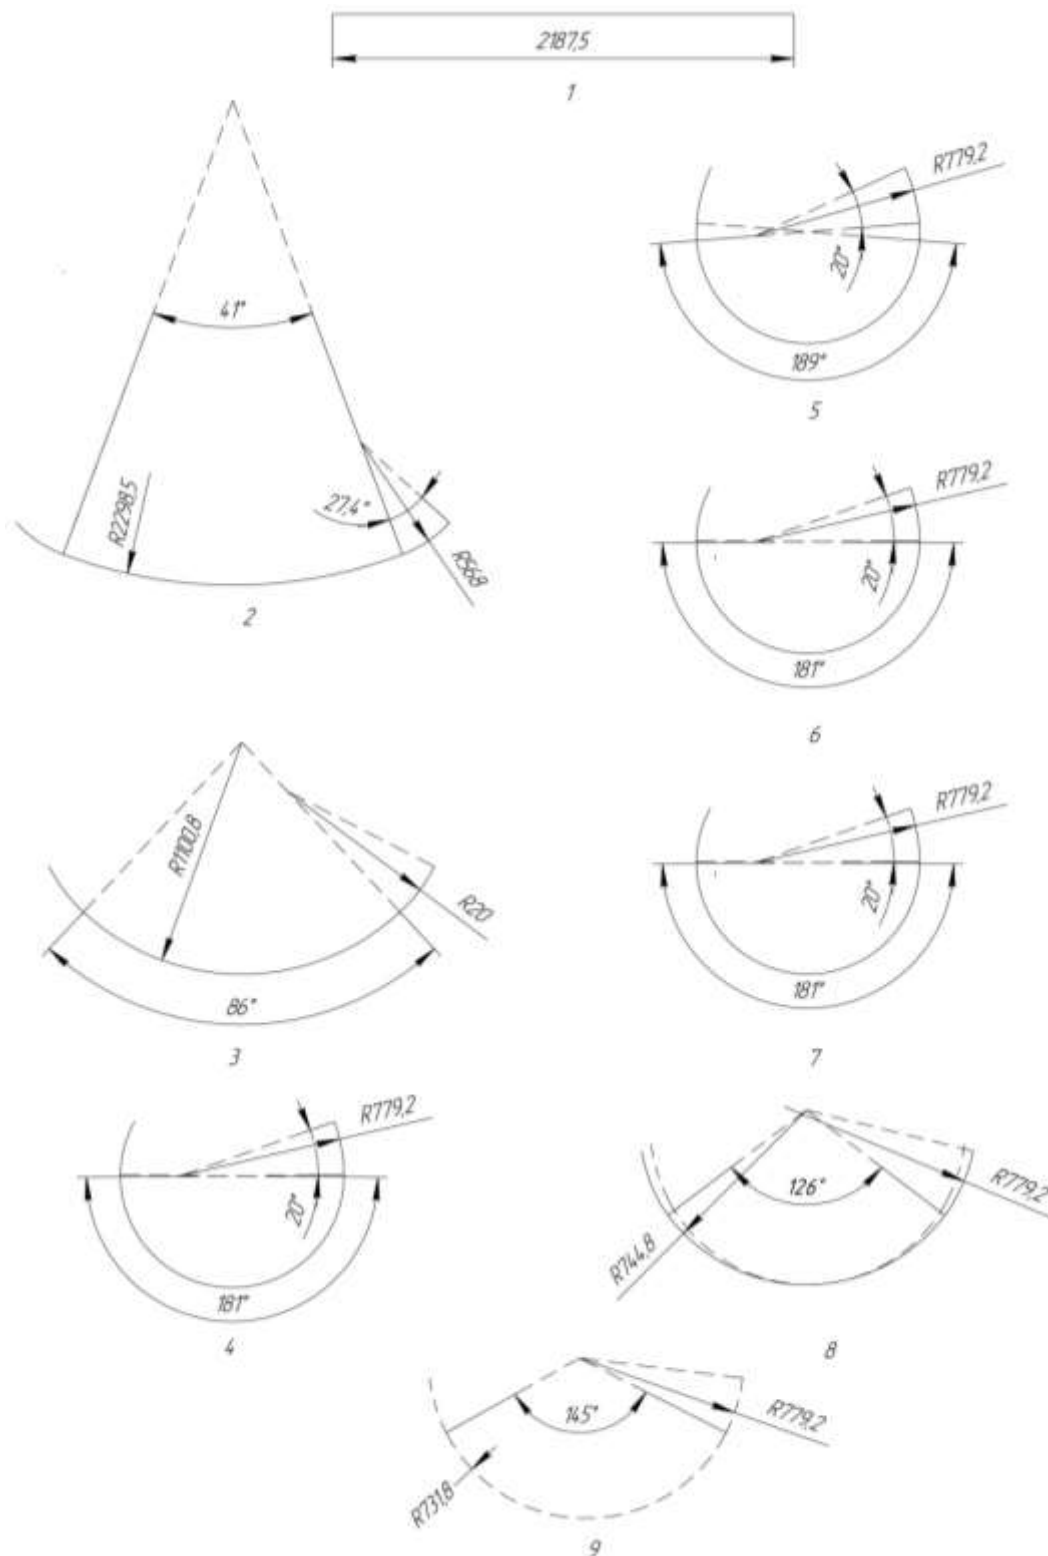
Усовершенствованная калибровка для формовки полуцилиндрических
